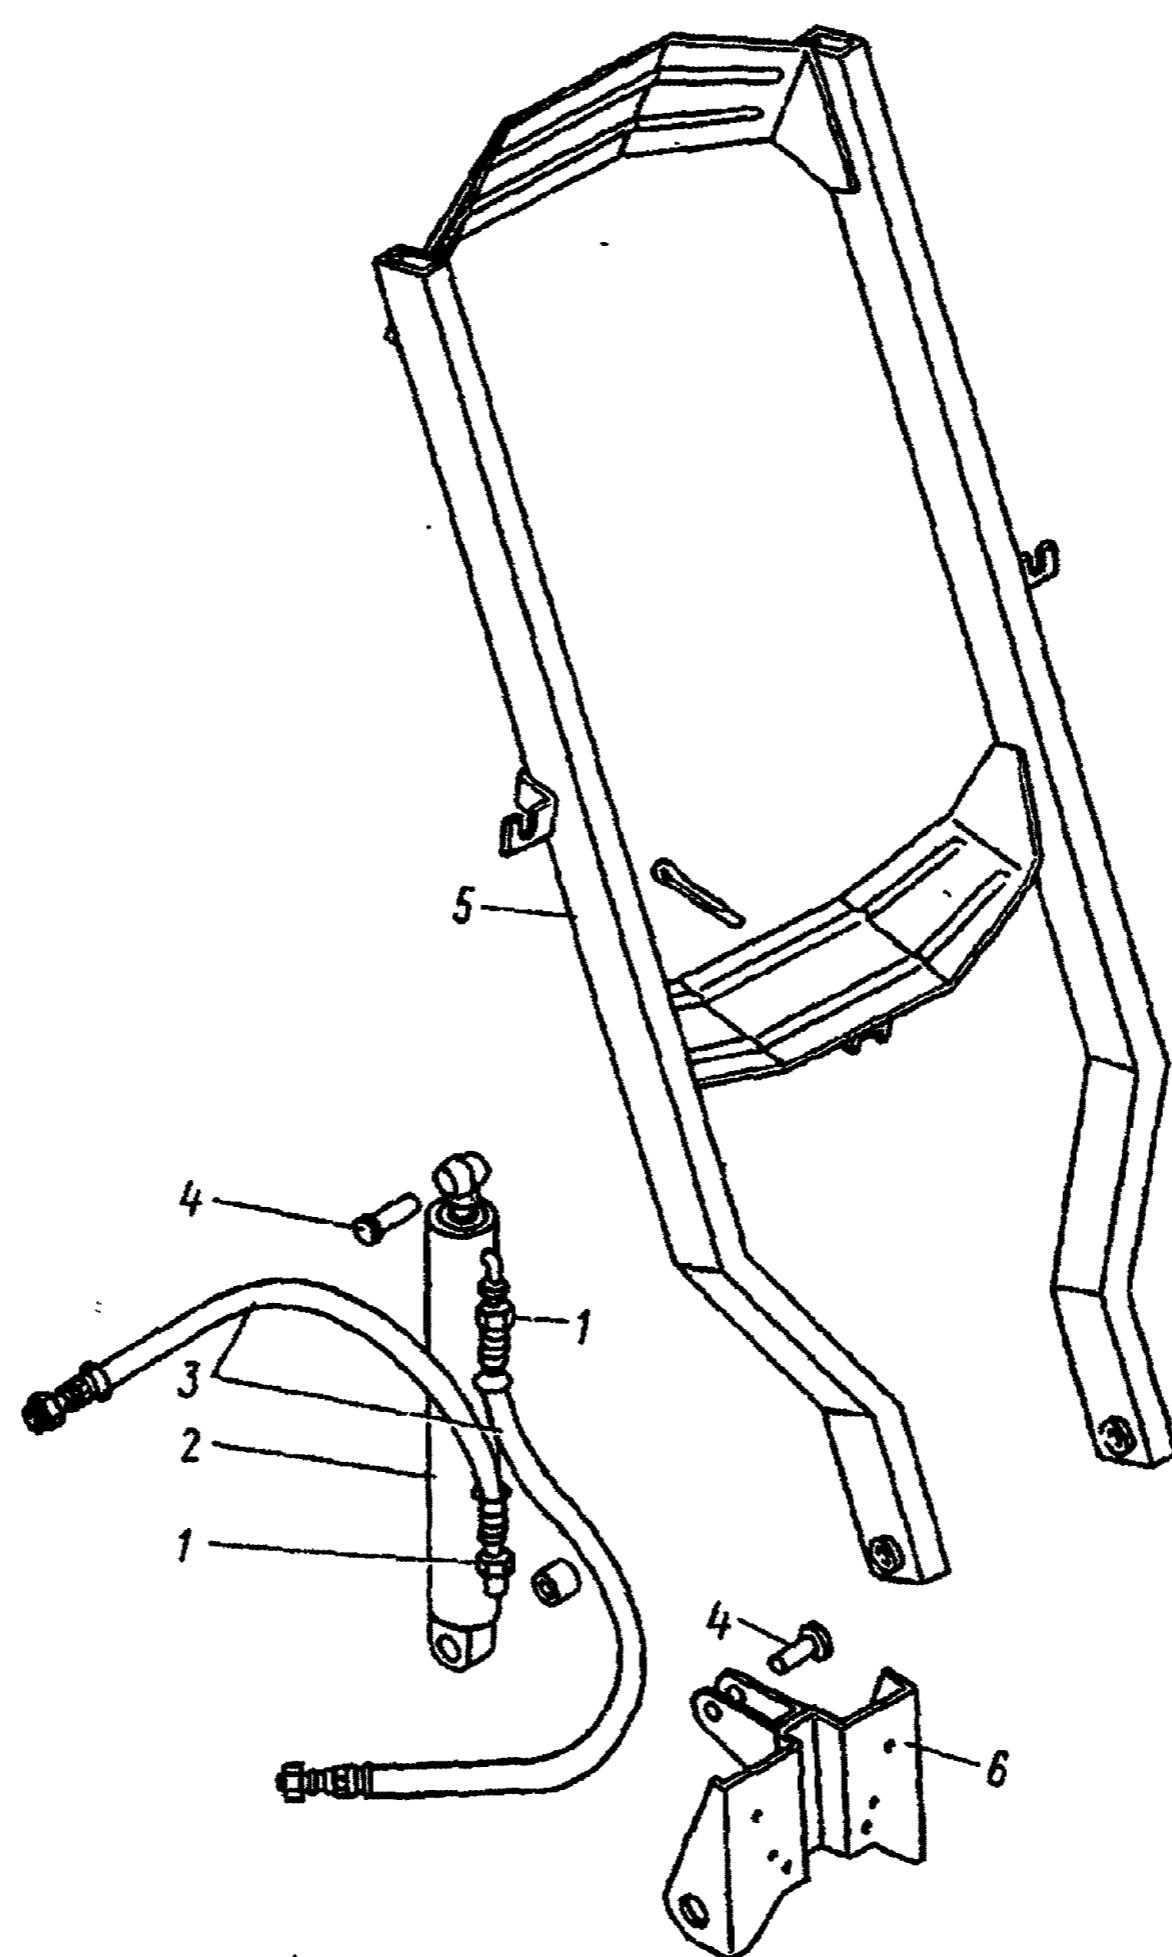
Гидроцилиндр механизма подъема запасного колеса:
